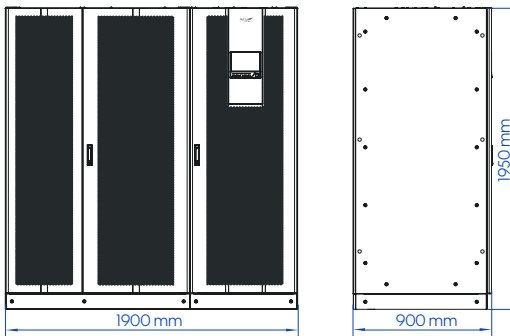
Dimensiones del UPS-IND HF 13800 (800 kVA)
